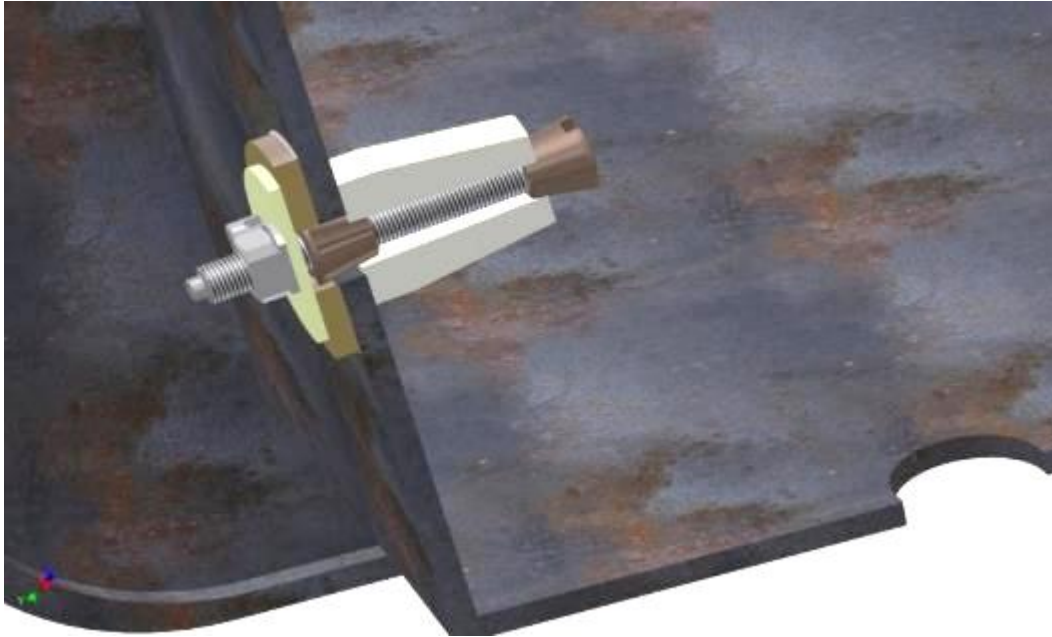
Der Block wird durch das Einbettwerkzeug an seinem Platz gehalten.
